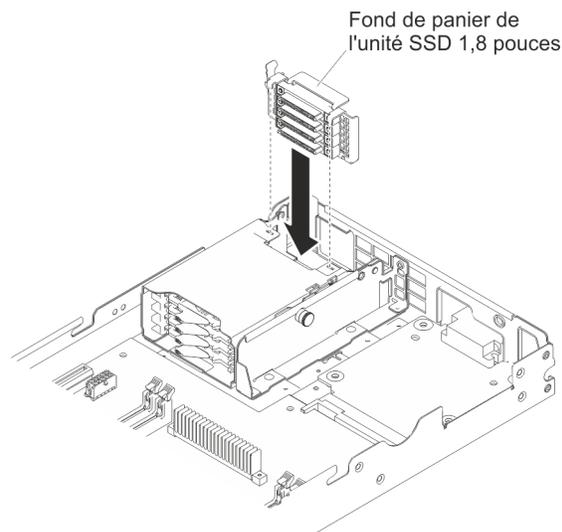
Installation de la plaque arrière pour les unités 1,8 pouces
